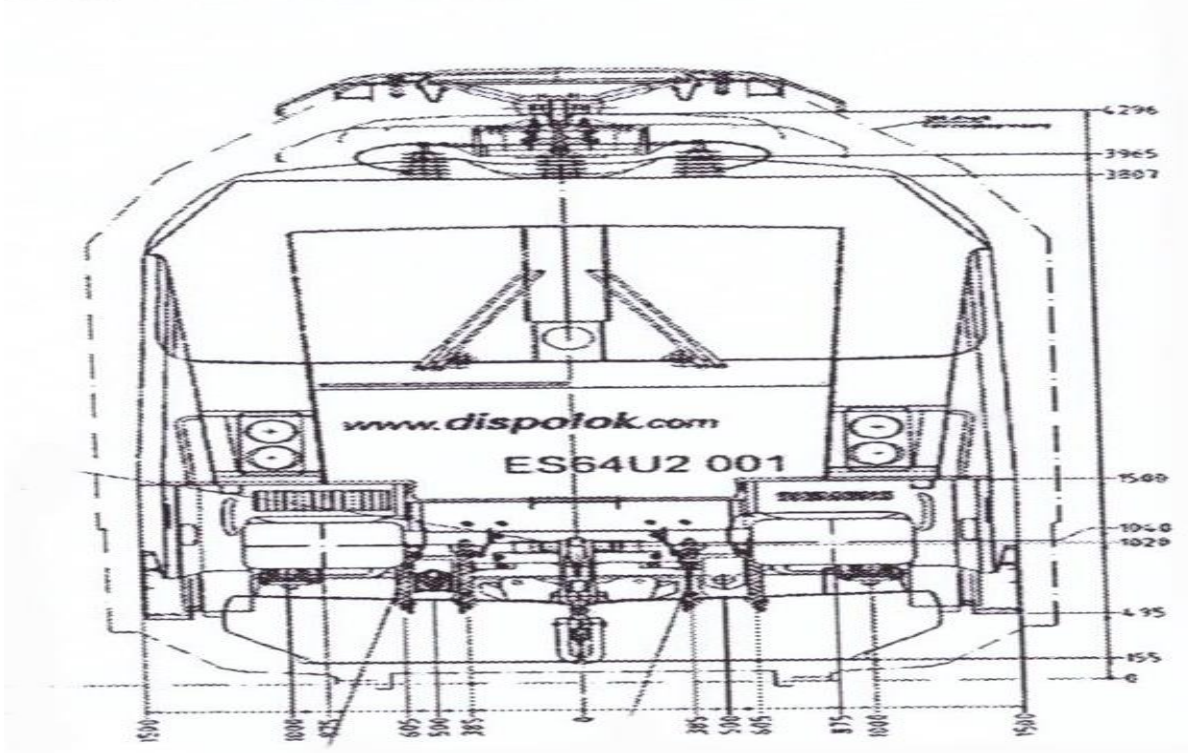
schița locomotivei cu principalele dimensiuni exterioare
